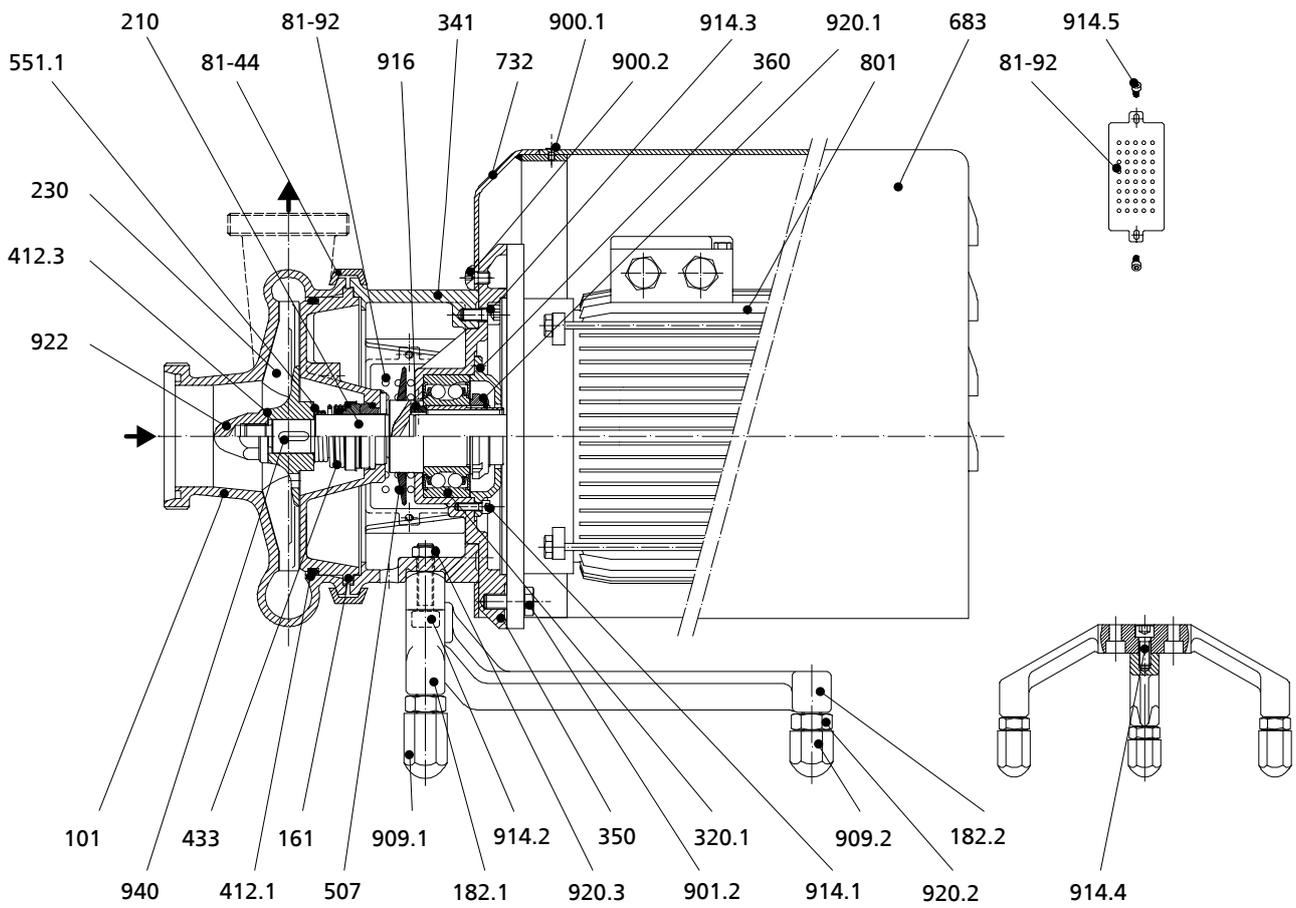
Gesamtzeichnung, Motorgröße IEC 71-112
